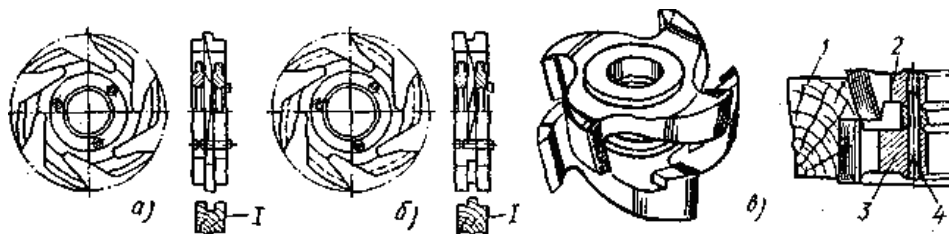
Складені фрези до чотирибічного поздовжньо-фрезерного верстата для обробки: а — паза, б — гребеня, в — деталей віконних плетінь; 1 — деталь, 2 — верхня фреза, 3 — нижня фреза, 4 — штифт; I — профілі оброблюваних деталей
